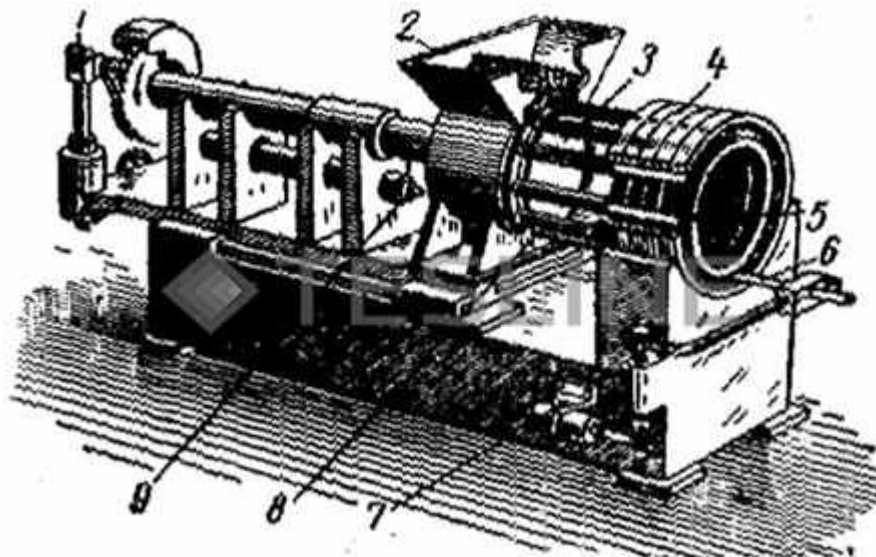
Схема нагревателя для концов заготовок со щелевым кольцевым индуктором:
